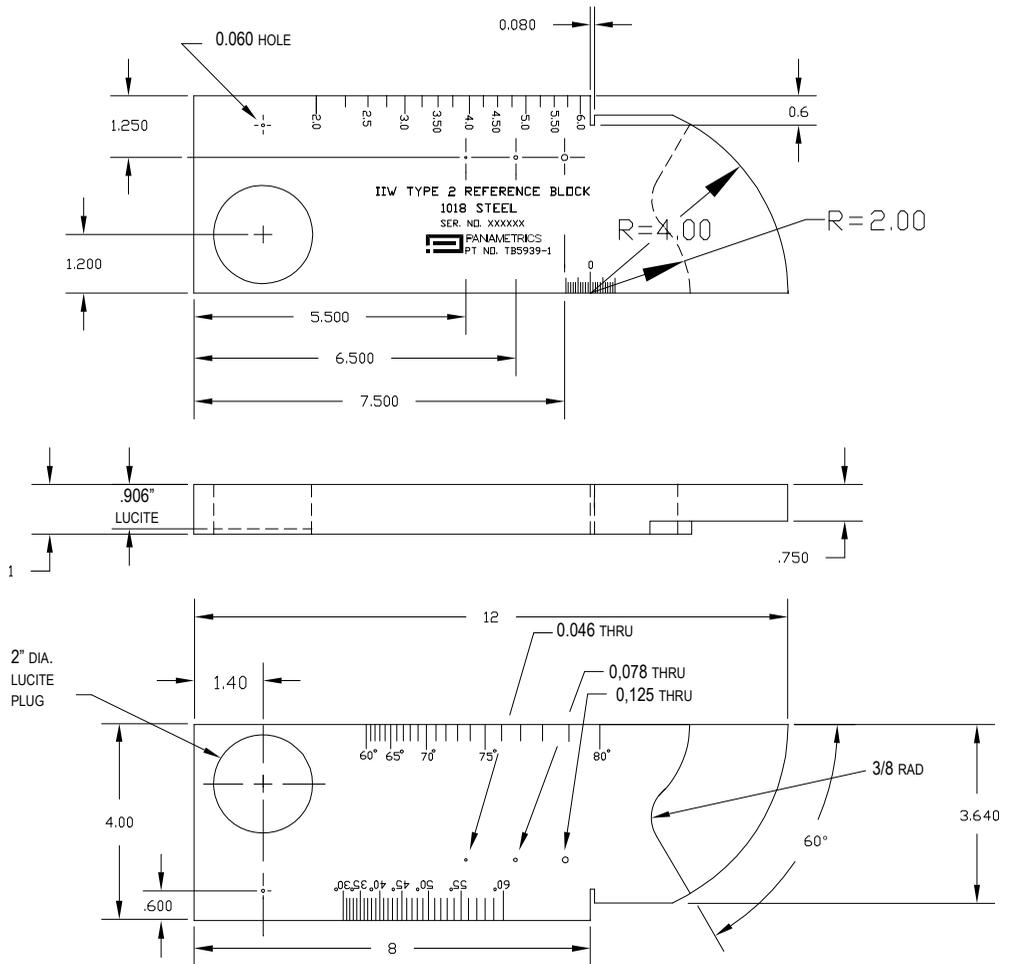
Калибровочный образец IIW type 2 (Арт.: TB5939-1)
